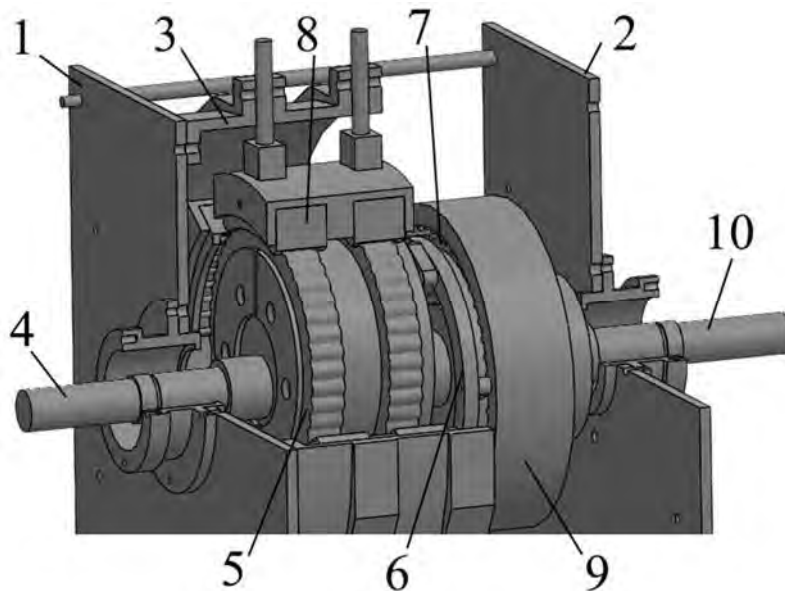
Плавнорегулируемая планетарная передача с двухвенцовым сателлитом: 1, 2 – пластины; 3 – обойма; 4 – вал ведущий; 5 – сателлит двухвенцовый; 6 – муфта Шмидта; 7 – сателлит одновенцовый; 8 – секторы; 9 – колесо цевочное; 10 – вал ведомый
